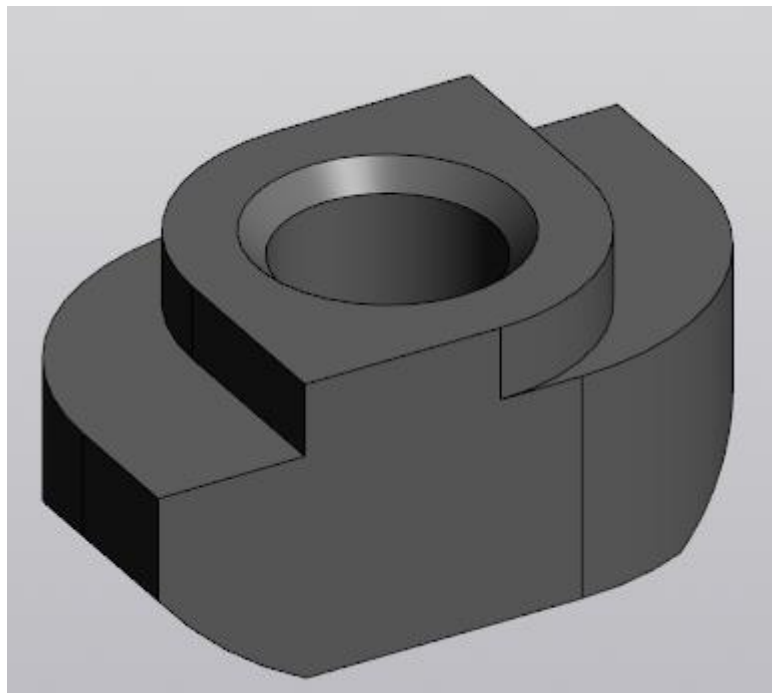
3D-модель гайки 20TN-M4.
